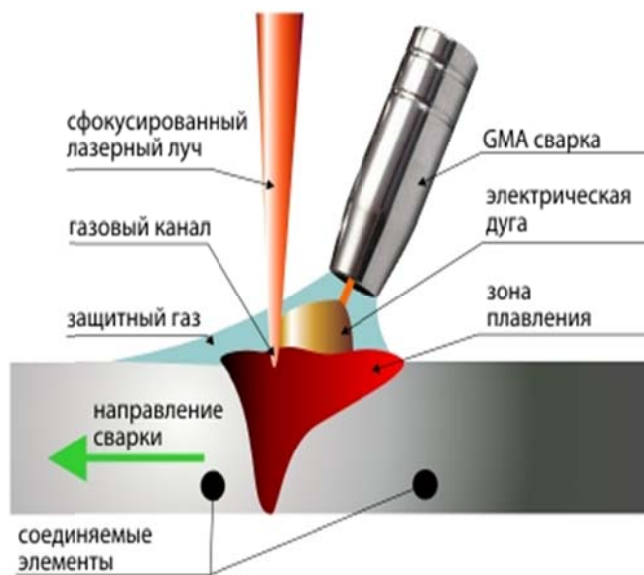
Схема процесса гибридной лазерно-дуговой сварки
